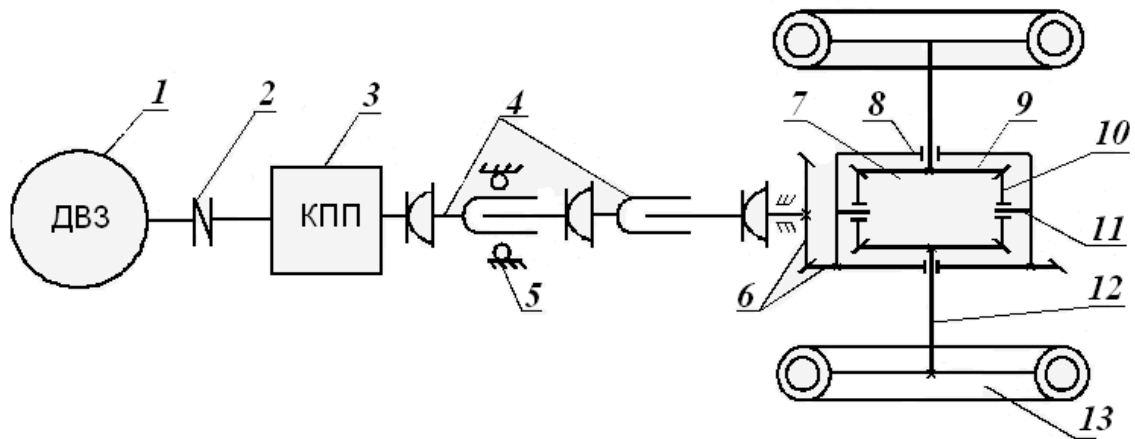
Кінематична схема трансмісії вантажного автомобіля: 1 - двигун; 2 - муфта зчеплення; 3 - коробка переми́ни передач; 4 - телескопічні карданні вали; 5 - проміжна опора; 6 - зубчасті колеса головної передачі; 7 - диференціал; 8 - корпус диференціала; 9 - хрестовина; 10 - сателіти; 11- зубчасті колеса півосей; 12 - півосі; 13- ведучі колеса
